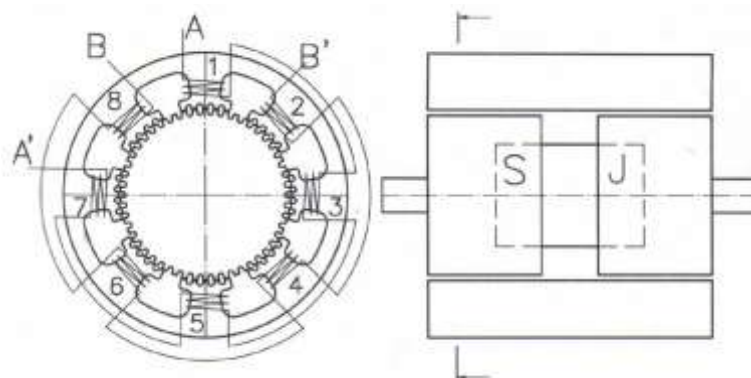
Motor s radiálně polarizovaným magnetem (Převzato z [17]).
